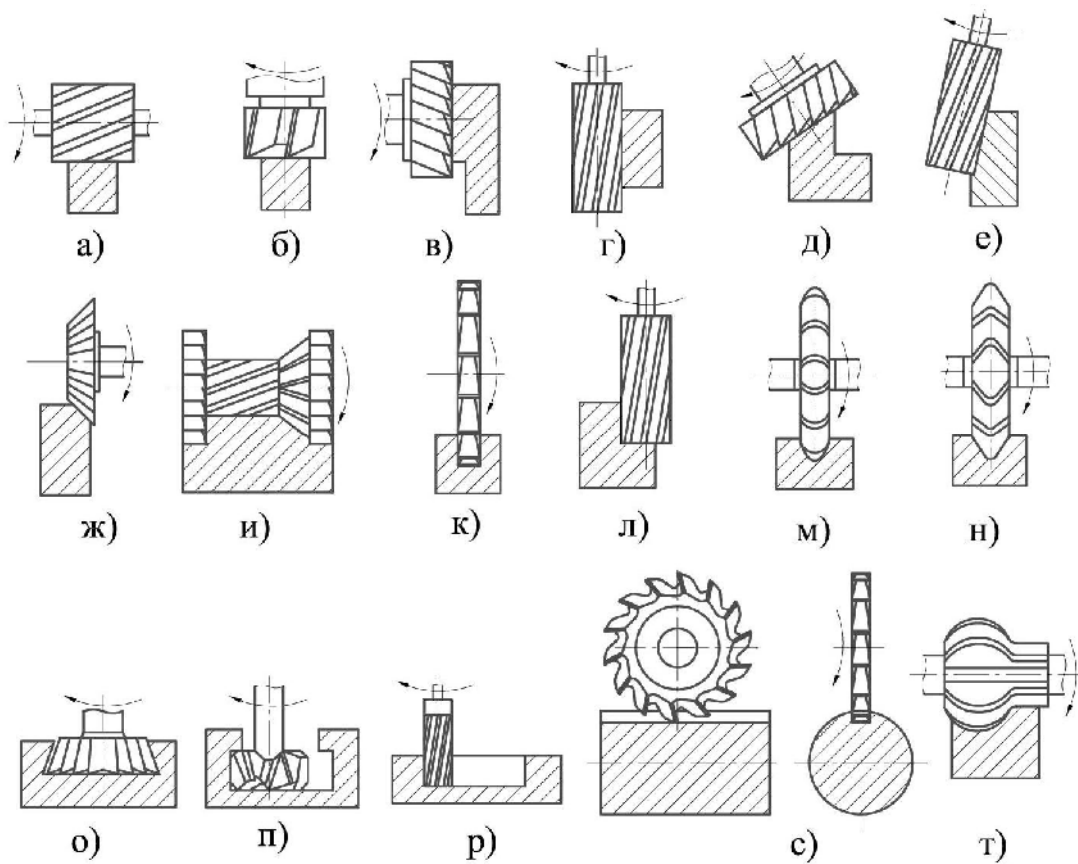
Схеми обробки поверхонь на фрезерних верстатах
